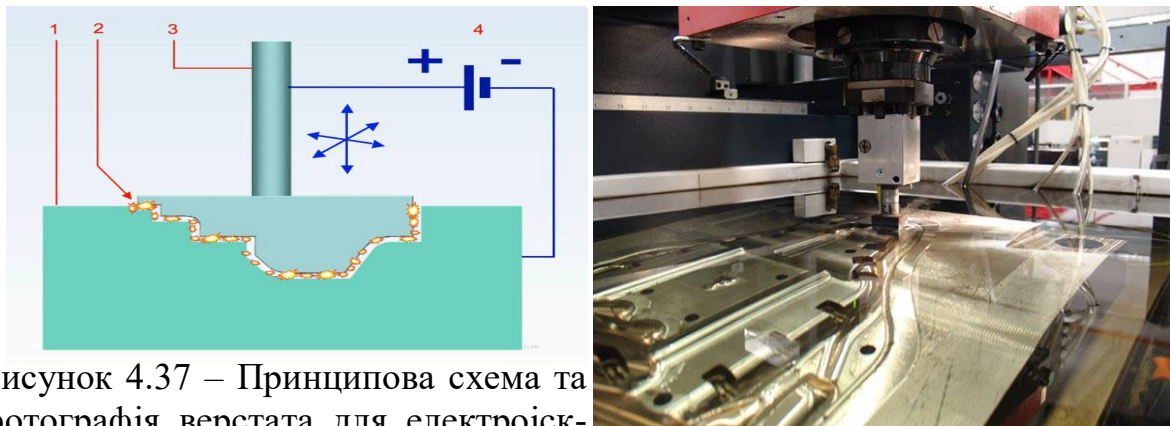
Принципова схема та фотографія верстата для електроіскрової обробки
